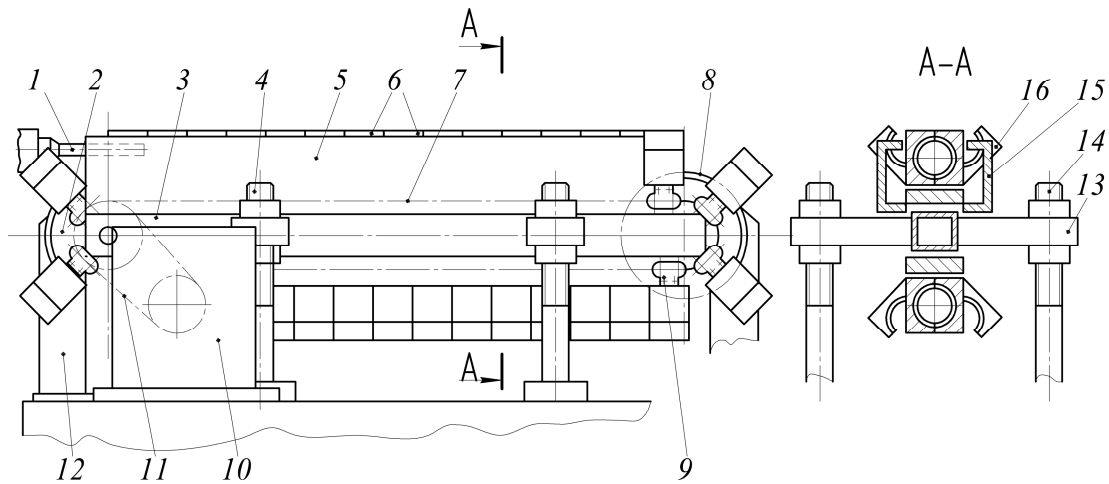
Принципова схема одноланцюгового гофратора: 1 – екструзійна головка; 2 – урухомна шестерня; 3 – траверса; 4 – колона; 5 – напрямна; 6 – півформа; 7 – робочий ланцюг; 8 – заднє лекало; 9 – каретка шестерень; 10 – редуктор урухомника; 11 – урухомна ланцюгова передача; 12 – переднє лекало
